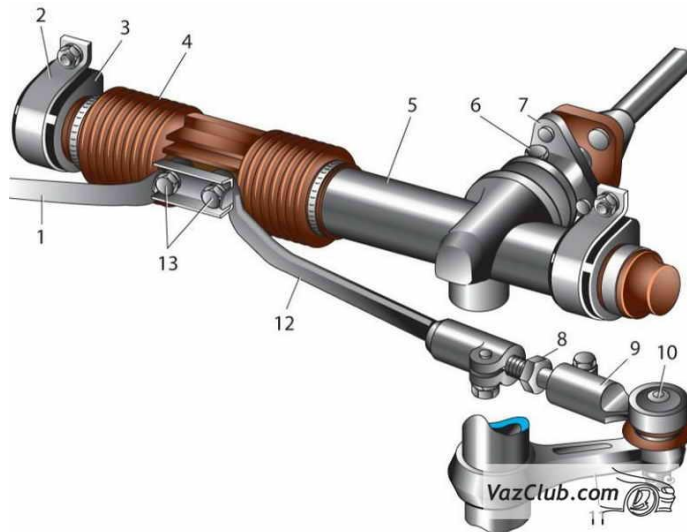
Рульовий механізм у зборі із приводом: 1, 12 – внутрішні наконечники рульових тяг 2 – скоба кріплення рульового механізму 3 – опора рульового механізму 4 – захисний чохол 5 – картер рульового механізму 6 – стяжний болт 7 – фланець еластичної муфти 8 – регулювальна тяга 9 – зовнішній наконечник рульової тяги 10 – кульовий шарнір наконечника 11 – поворотний важіль 13 – болти кріплення внутрішніх наконечників рульових тяг до рейки.
